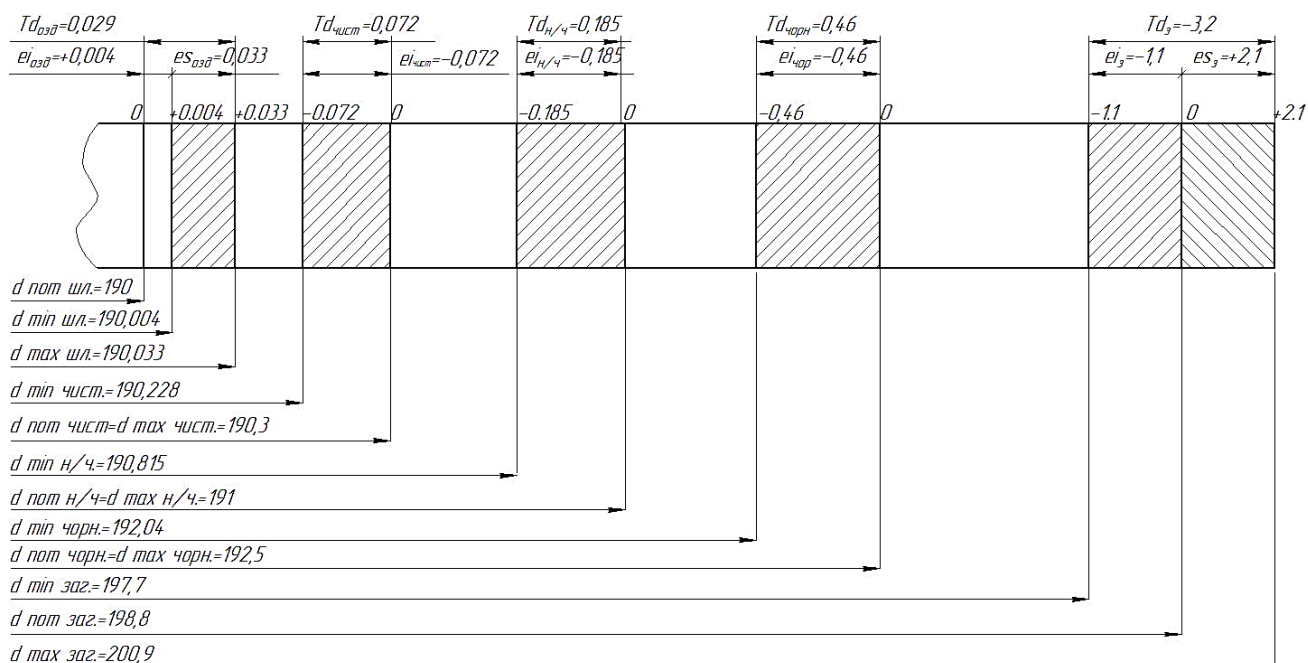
Схема розміщення полів припусків і допусків на оброблення зовнішньої циліндричної поверхні $\varnothing 190k6$
